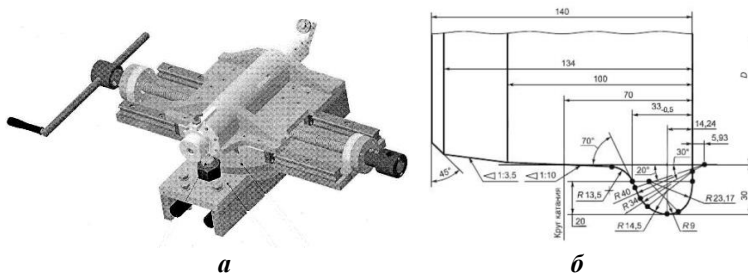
а) модель конструкции станка для обточки колёсных пар с ручной подачей, б) пример профиля бандажа колеса локомотива
